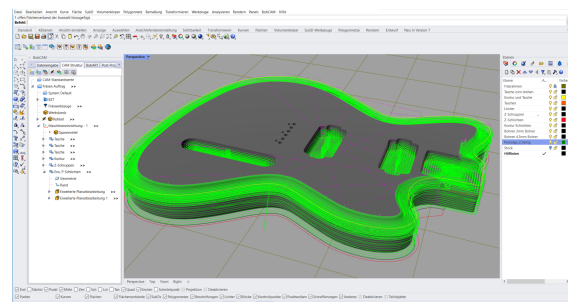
Berechnete Fräsbahnen in BobCAM zur maschinellen Fertigung des Bauteils.
